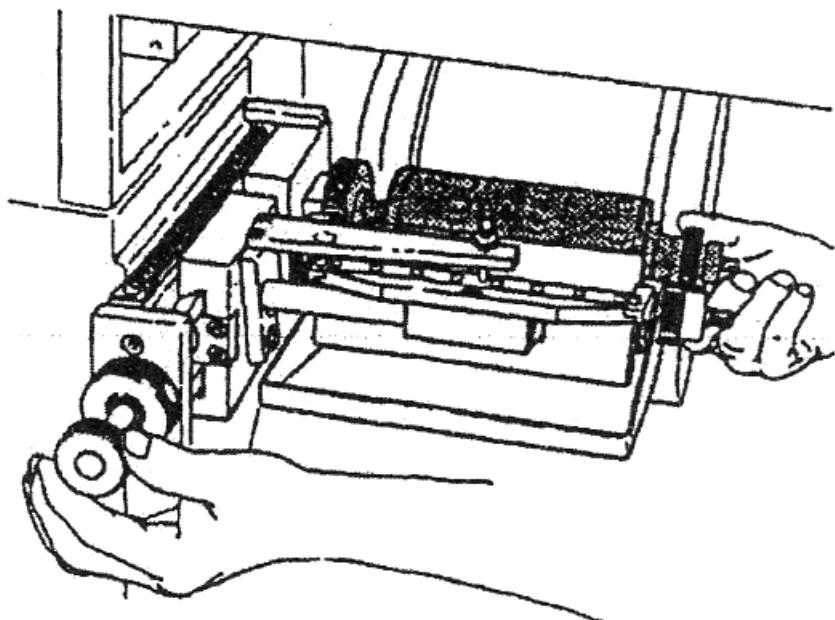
Регулировка прижима анилоксового вала к печатной форме на формном цилиндре
